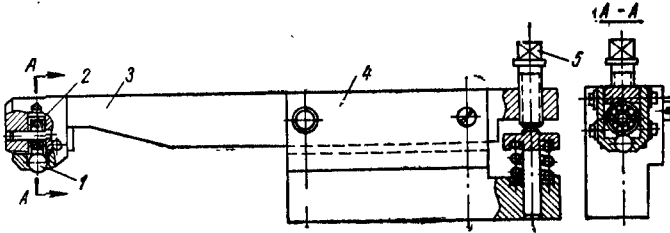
Раскатка для обработки отверстий диаметром 60—130 мм.
